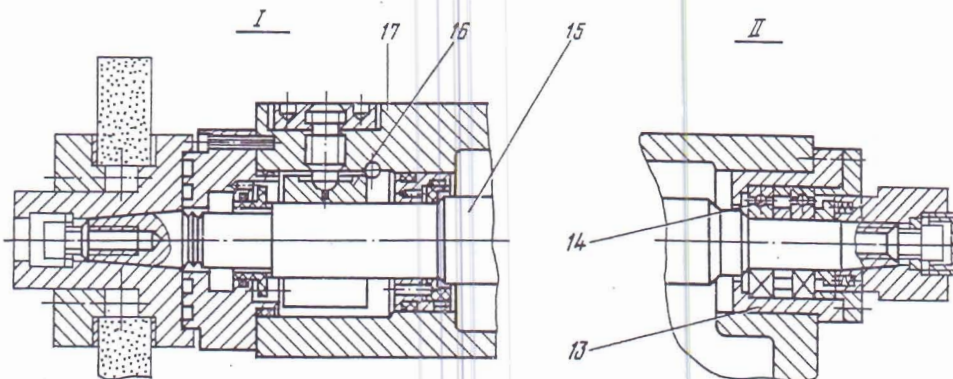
Шпиндель шлифовальной головки для станков ЗЕ711ВФ1, ЗЕ721АФ1-1, ЗЕ711АФ1, ЗЕ710А
